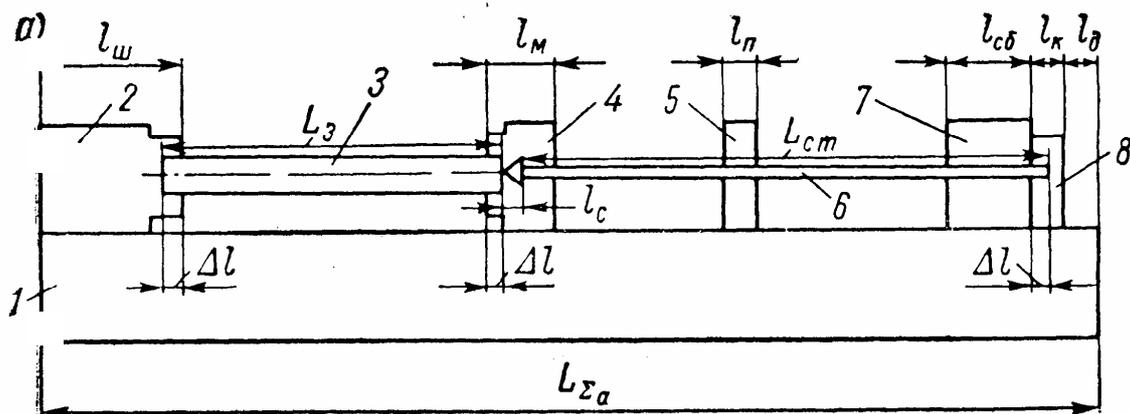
Схема обработки зеркала цилиндра на токарном станке или станке для глубокого растачивания токарного типа:
